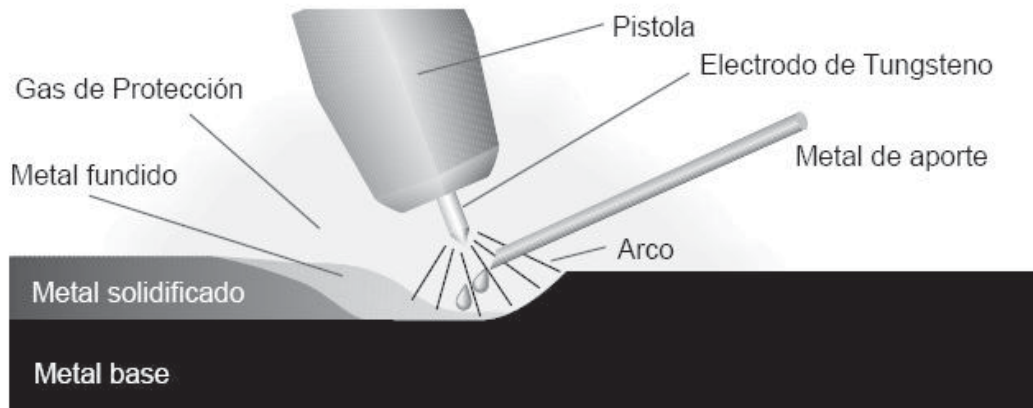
11 Esquema del proceso de la soldadura por arco de tungsteno y gas inerte.
